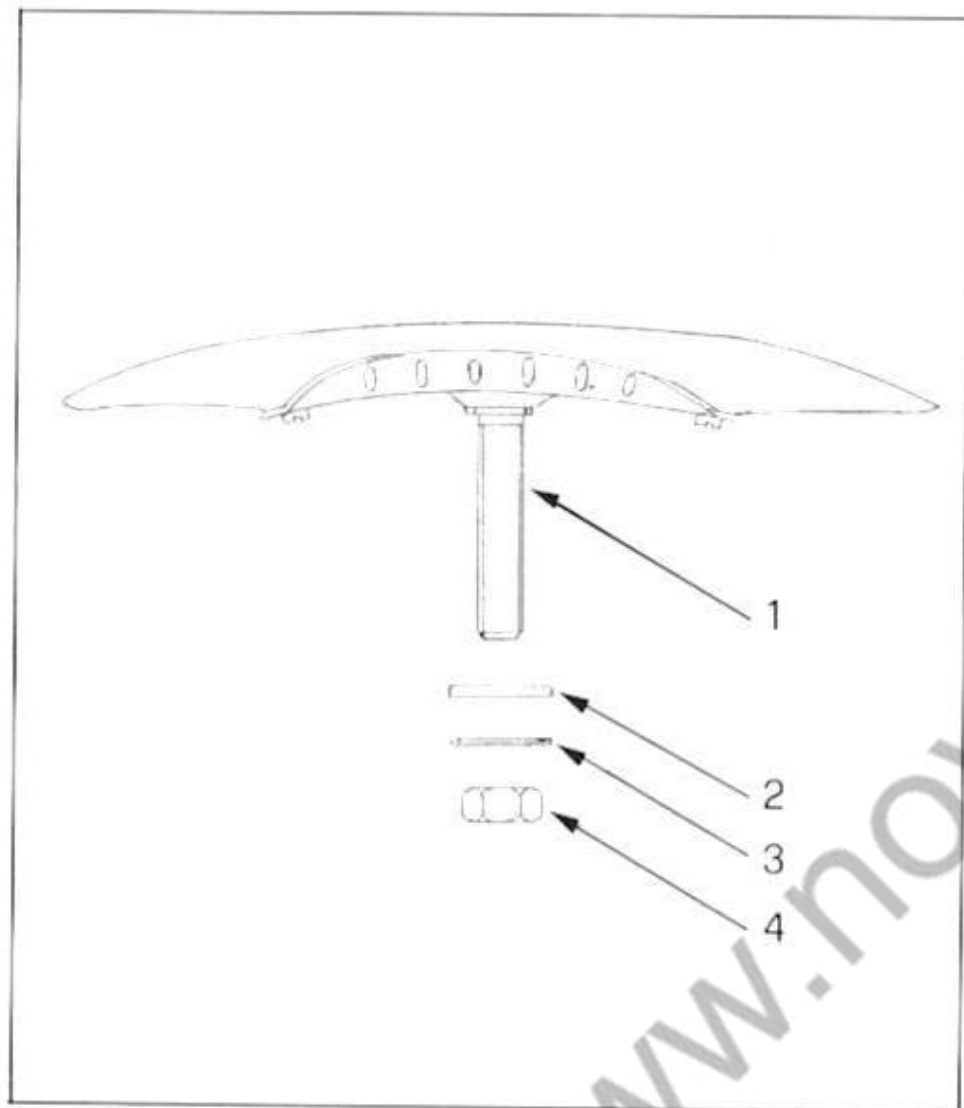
STAFFA FISSAGGIO PNEUMATICO
